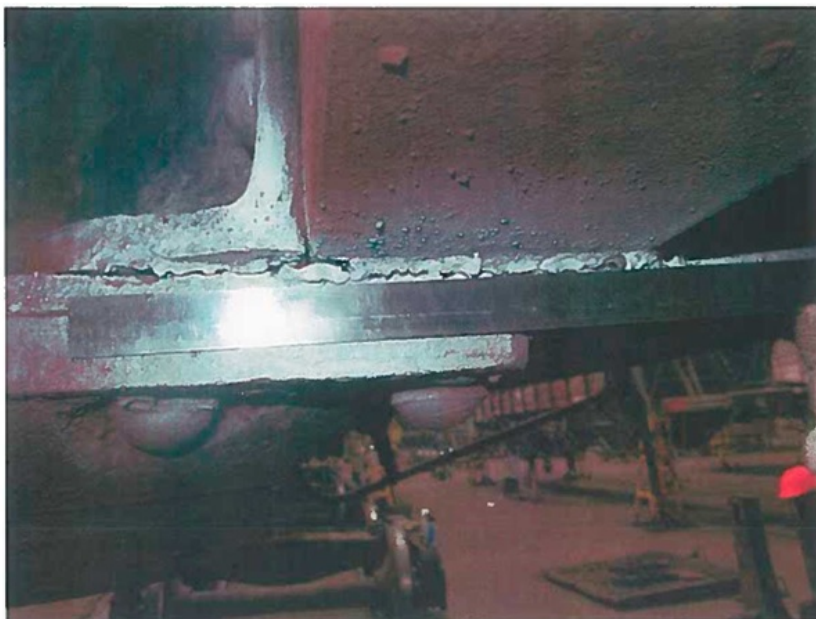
Тріщина в зварному шві який з'єднує хребтову балку з шворневою
